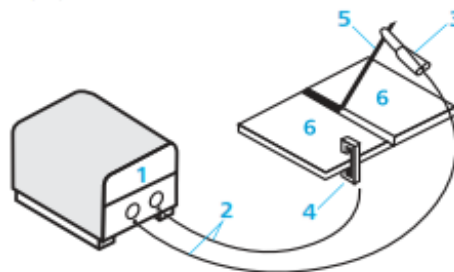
Equipo de Soldadura por Arco Eléctrico
